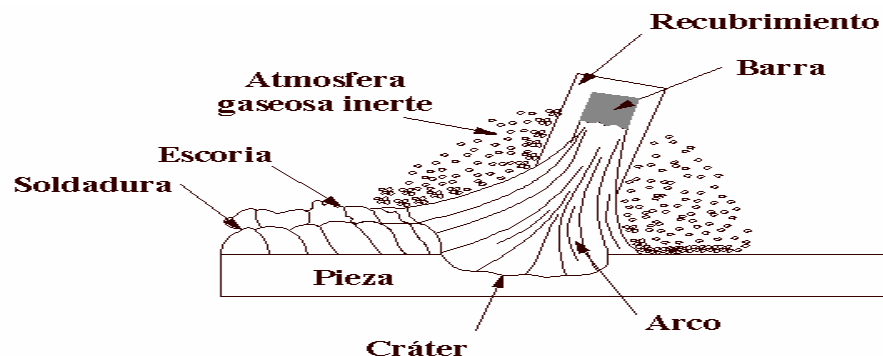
Variables que influyen en la soldadura por arco eléctrico.
